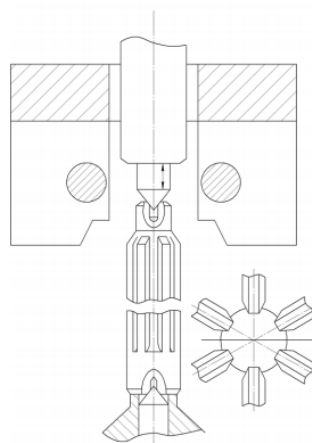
Схема восстановления шлицевой поверхности вала вдавливанием с помощью шлиценакатной головки
